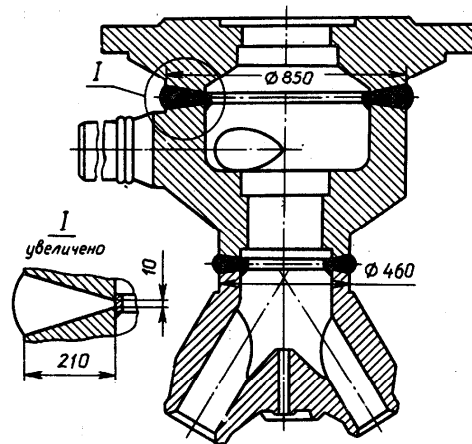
Коробка клапана автоматического затвора турбины из кованных деталей из аустенитной стали
